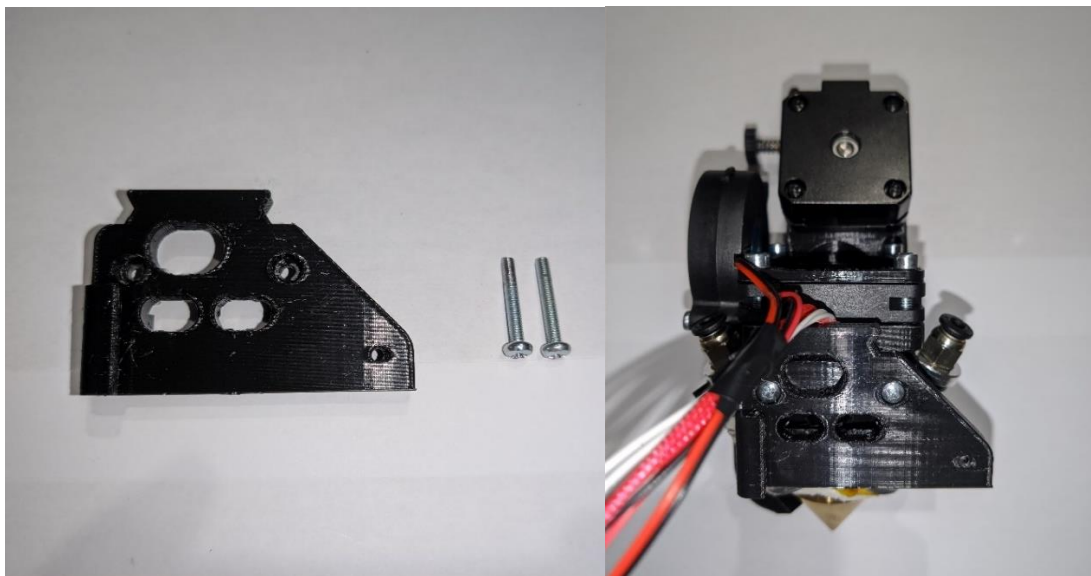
Junção do adaptador ao conjunto do bico extrusor.
